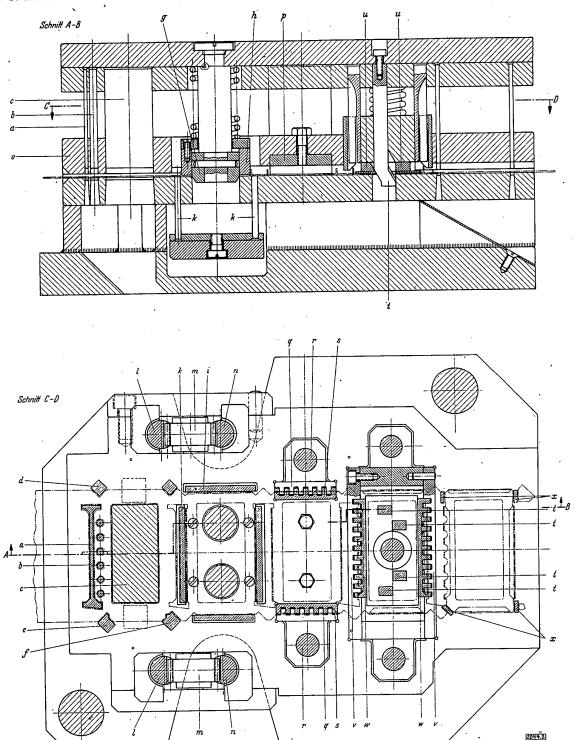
Folgewerkzeug für Werkstück nach Bild 1 im Senkrecht- und Waagerechtschnitt
